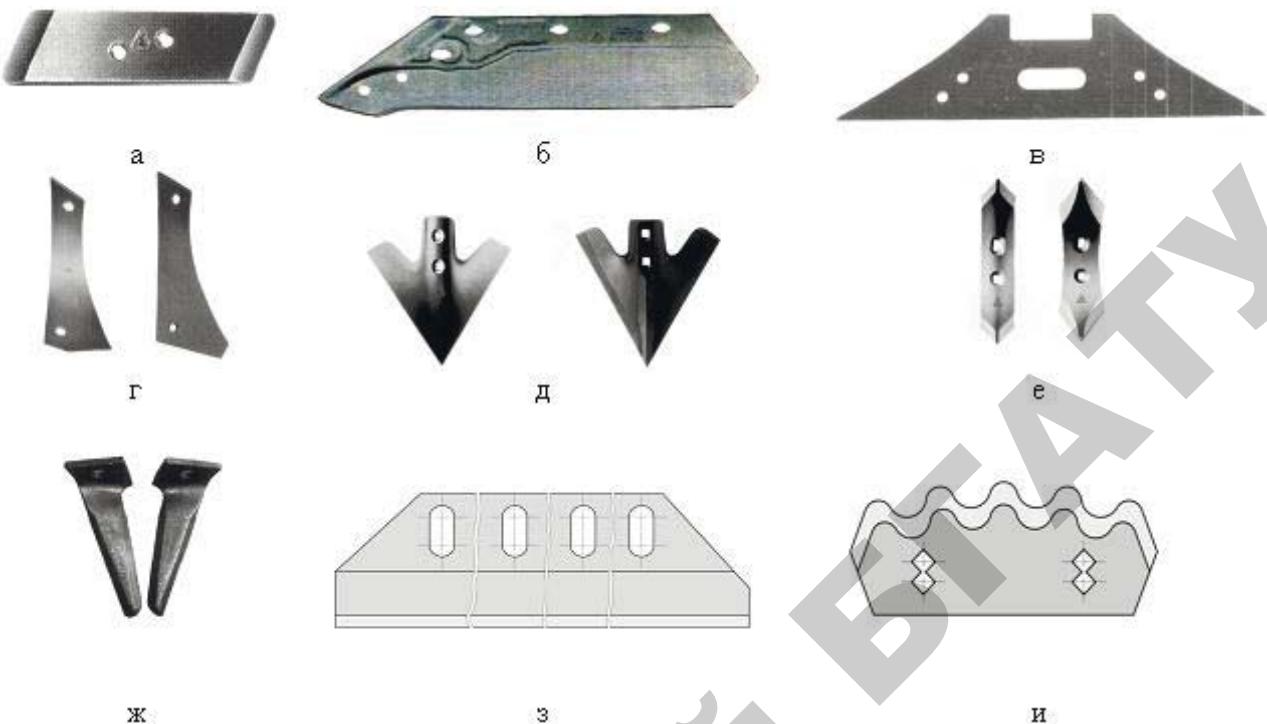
Типовые представители сменных ДРОМ почвообрабатывающих и кормоуборочных машин:
